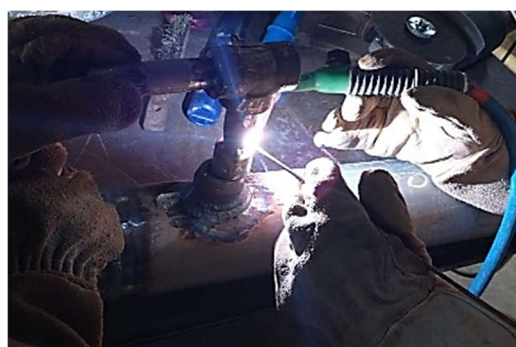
(d) - Execução de soldagem das conexões auxiliares [Autor, 2022].
